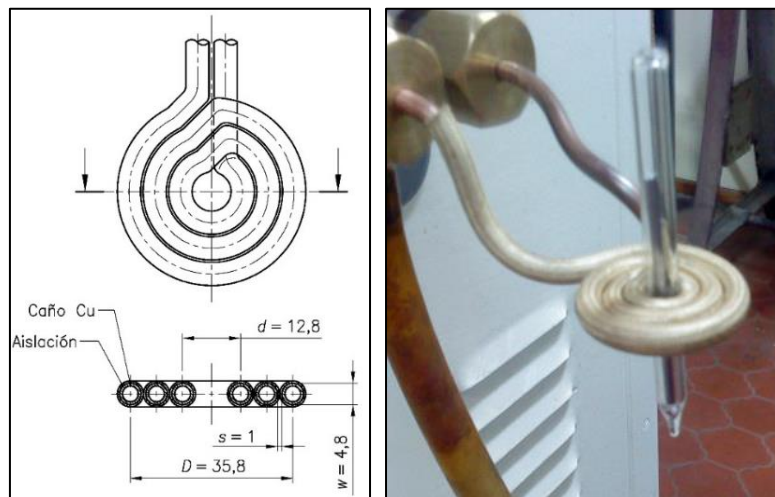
a) Dimensiones del inductor plano diseñado. b) Inductor plano acoplado a la máquina.
